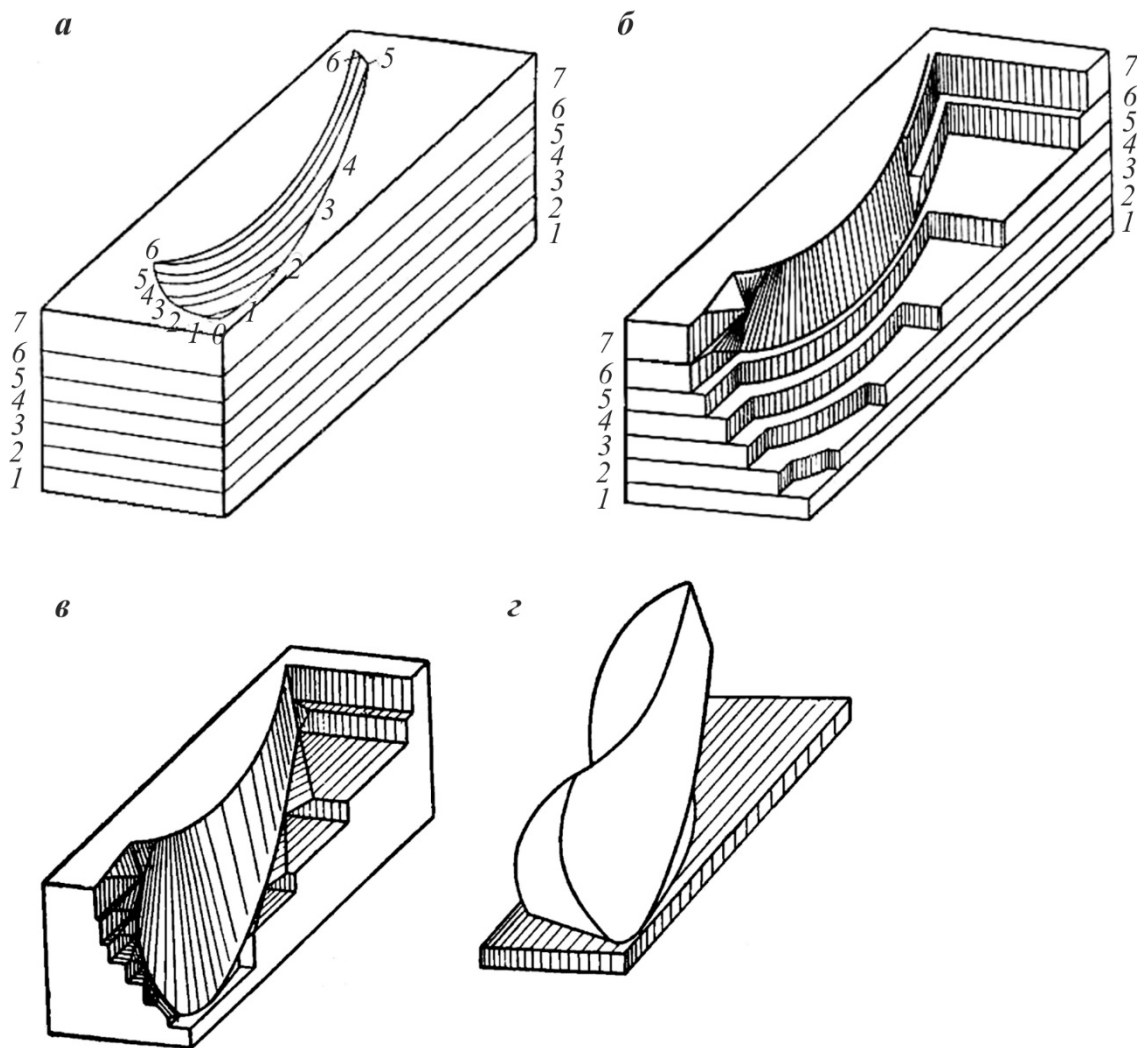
Заготівка й виготовлення моделей профілю лопатки робочого колеса гідротрансформатора
